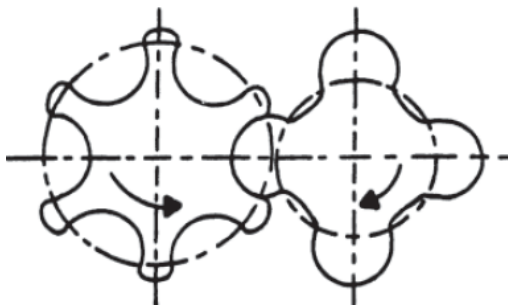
Vista de un corte de los rotores hembra y macho (Stoecker, 1998)
